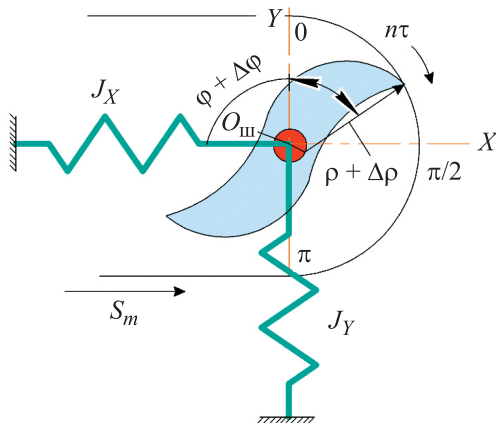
Модель процесса фрезерования двухканавочной фрезой (S_m — минутная подача инструмента)
